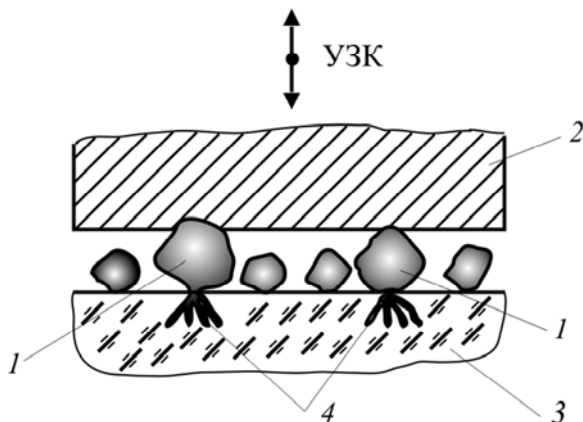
Схема взаимодействия абразивных зерен с поверхностью заготовки и инструмента в процессе ультразвуковой размерной обработки:
